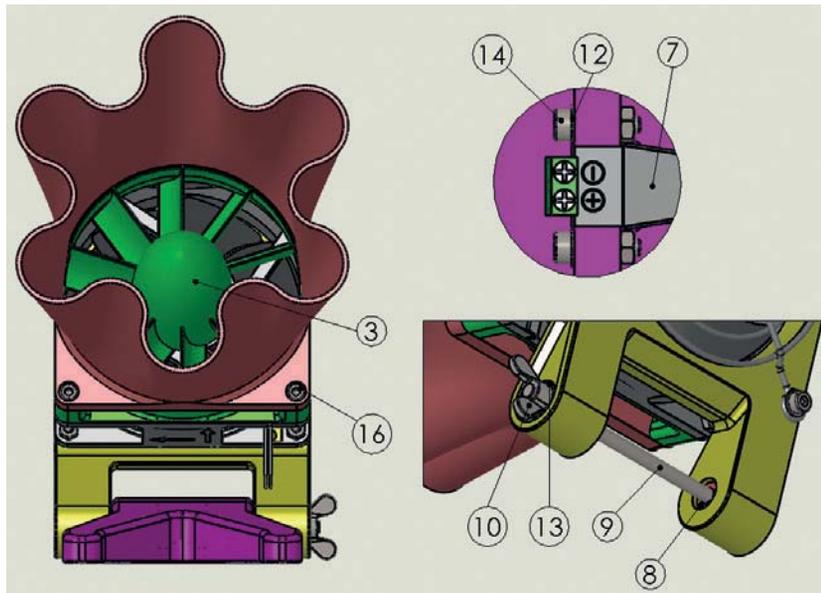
Bauteile für den Zusammenbau des Ventilators (Teil 2)
